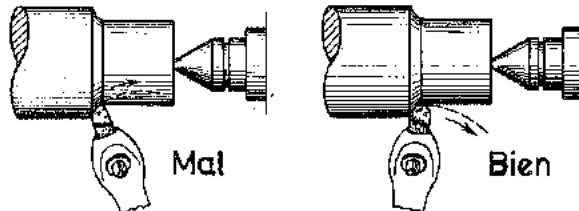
Modos erróneo y correcto de posicionar el soporte de herramientas para pasadas profundas (South Bend Lathe Works).
